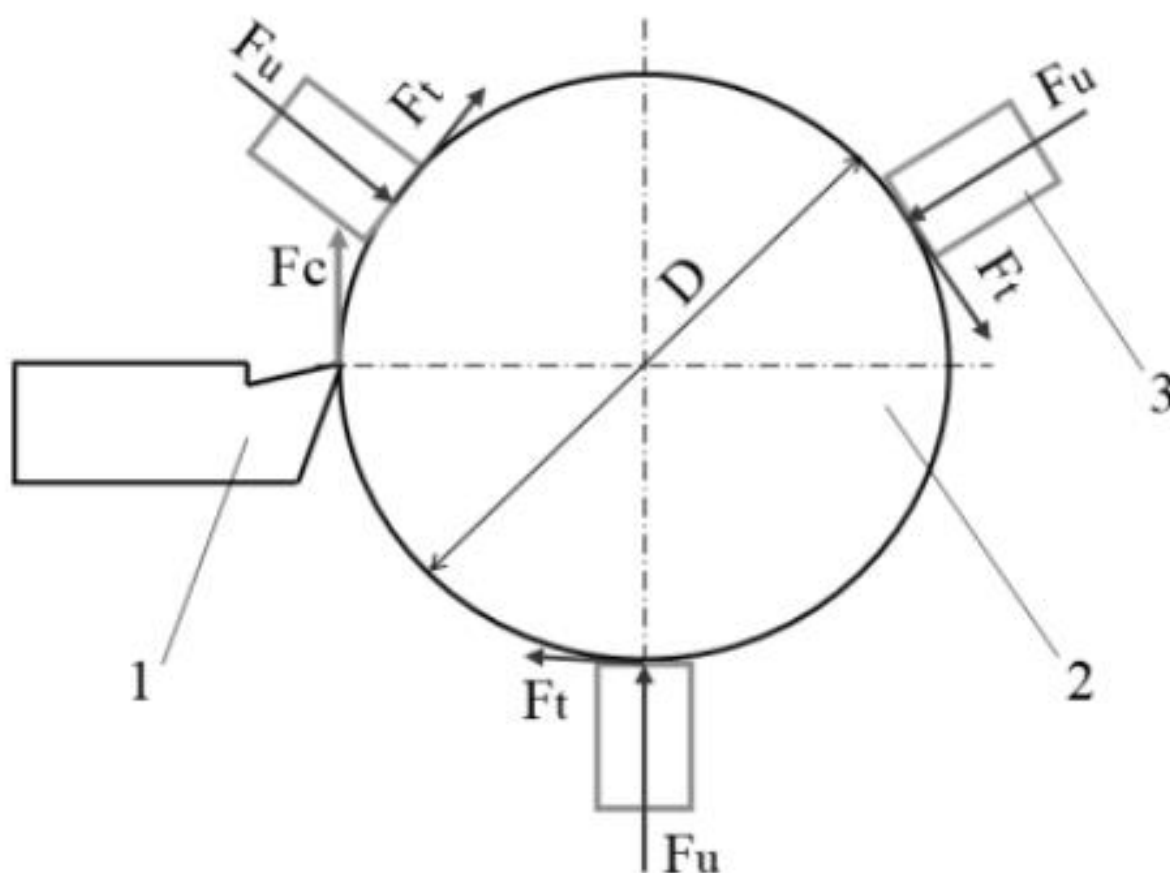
Усилие, действующее на заготовку, зажатую в зажимном патроне с 3 кулачками 1 - режущий инструмент, 2 - заготовка, 3 кулачка [5]
